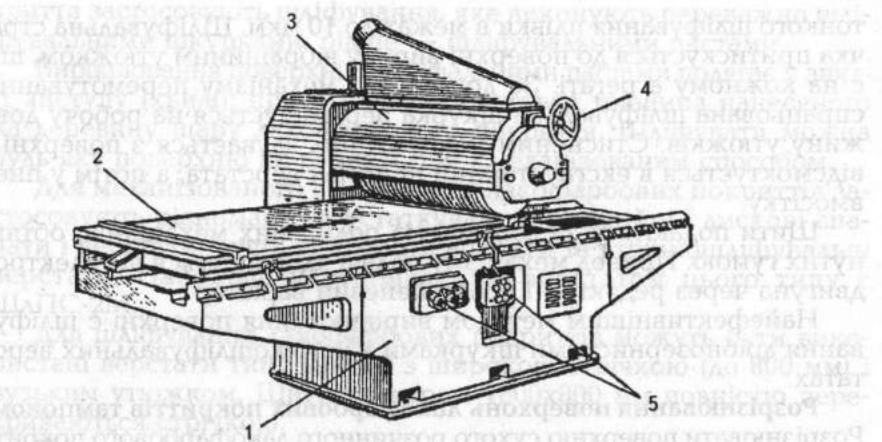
Однобарабанний полірувальний верстат ПІБ:
